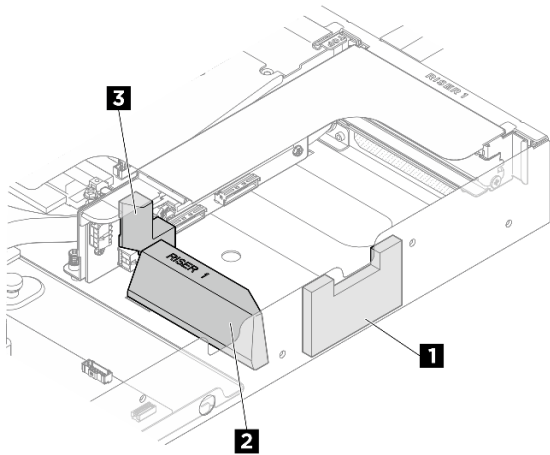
Position der DPU-Luftführung im Steckplatz für Adapterkarte 1
